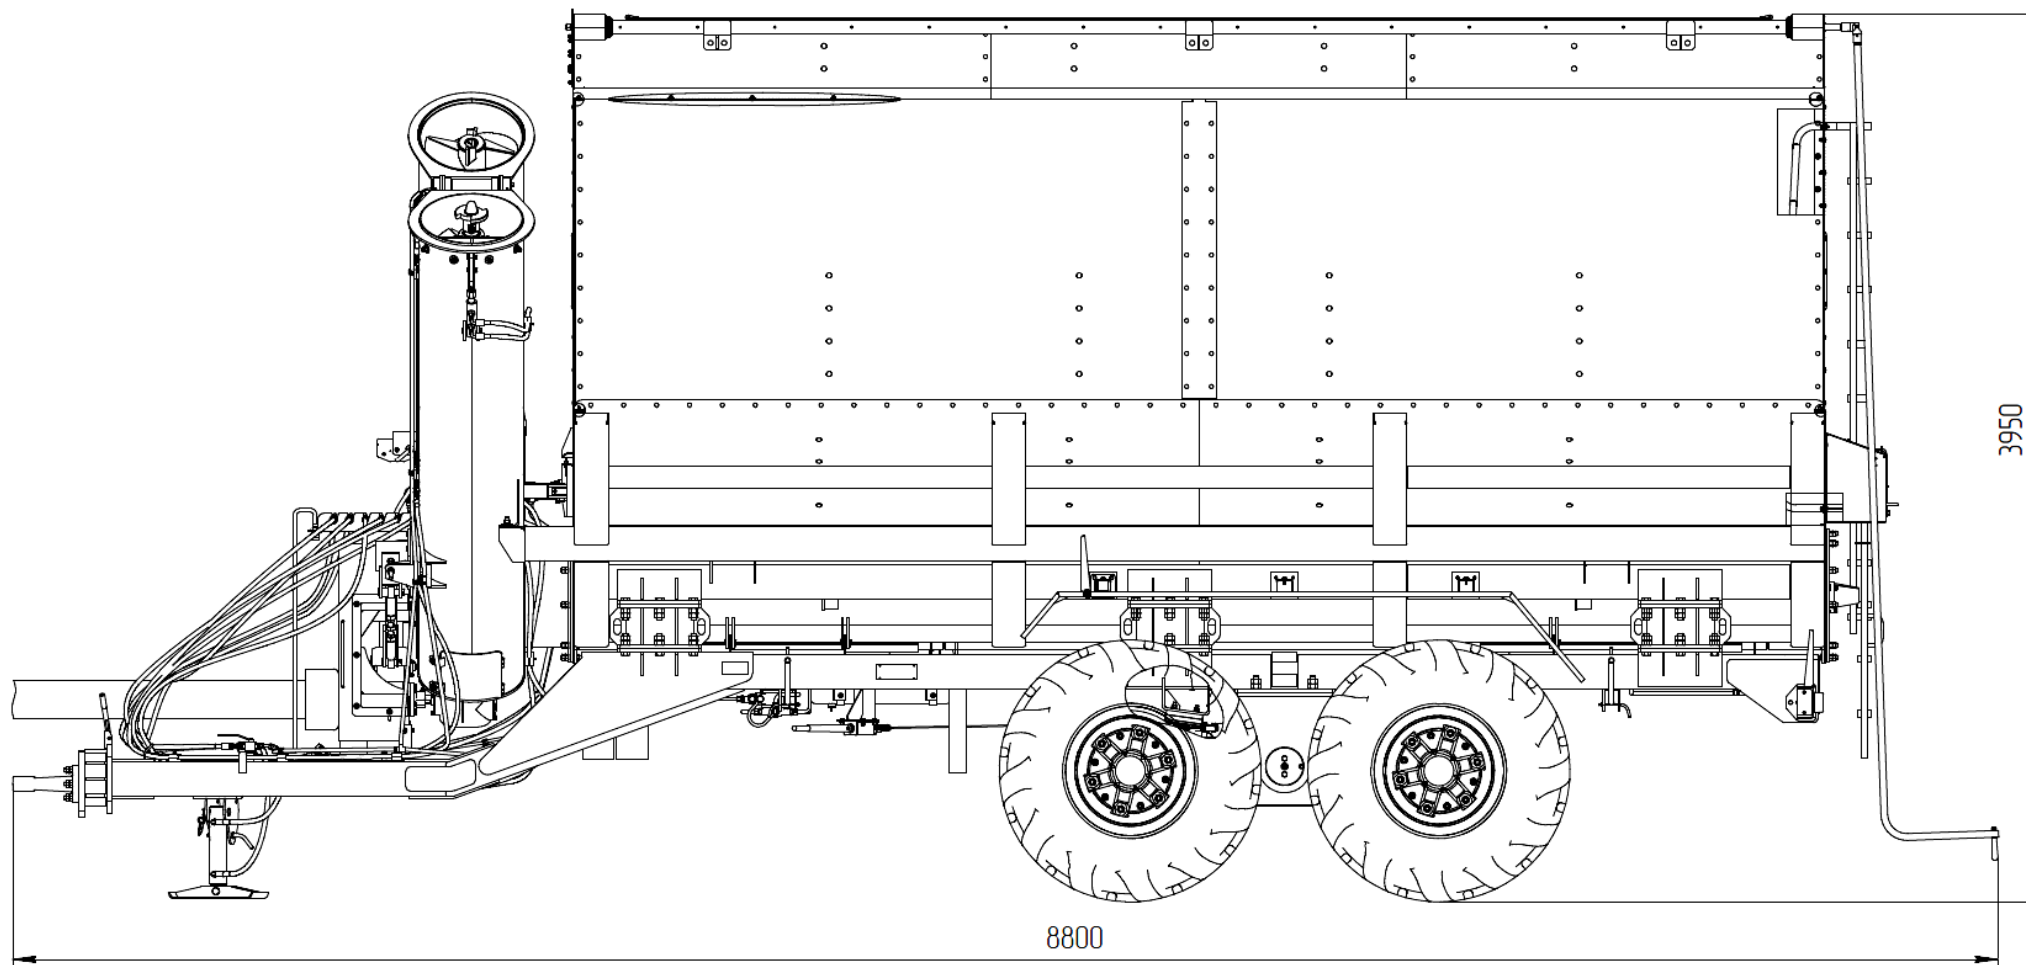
а – Габаритные размеры бункера в транспортном положении
